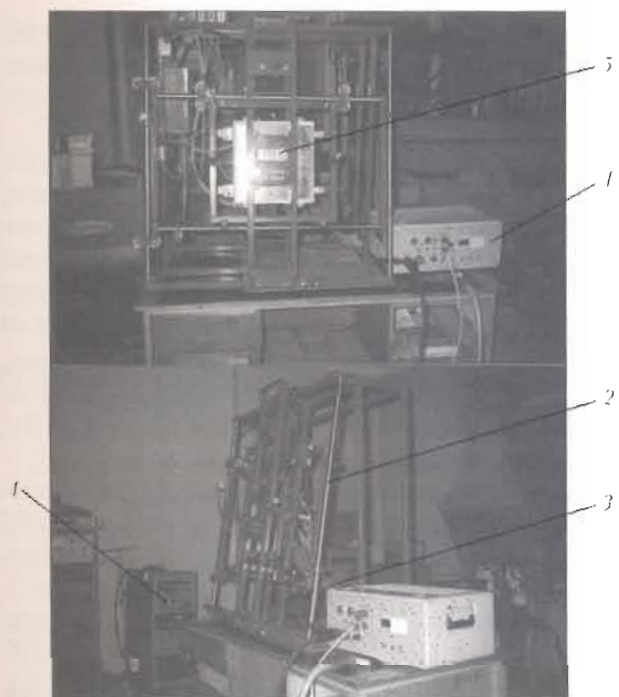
Лабораторная установка для отработки технологии ДТС трехслойной панели с ячеистым наполнителем: 1 — источник сварочного тока; 2 — сварочный стенд; 3 — соединительные кабели; 4 — блок управления сварочным циклом; 5 — рамка с образцом
